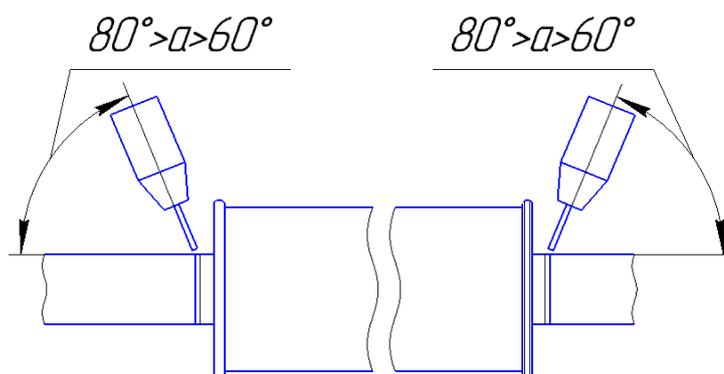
Сварка дополнительного глушителя с задней трубой и средней
